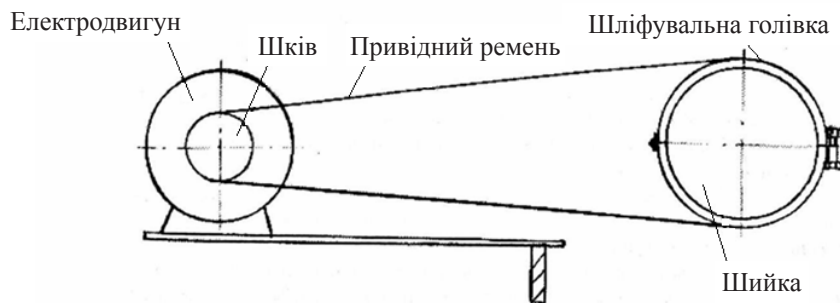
Схема пристрою для шліфування шатунної шийки
